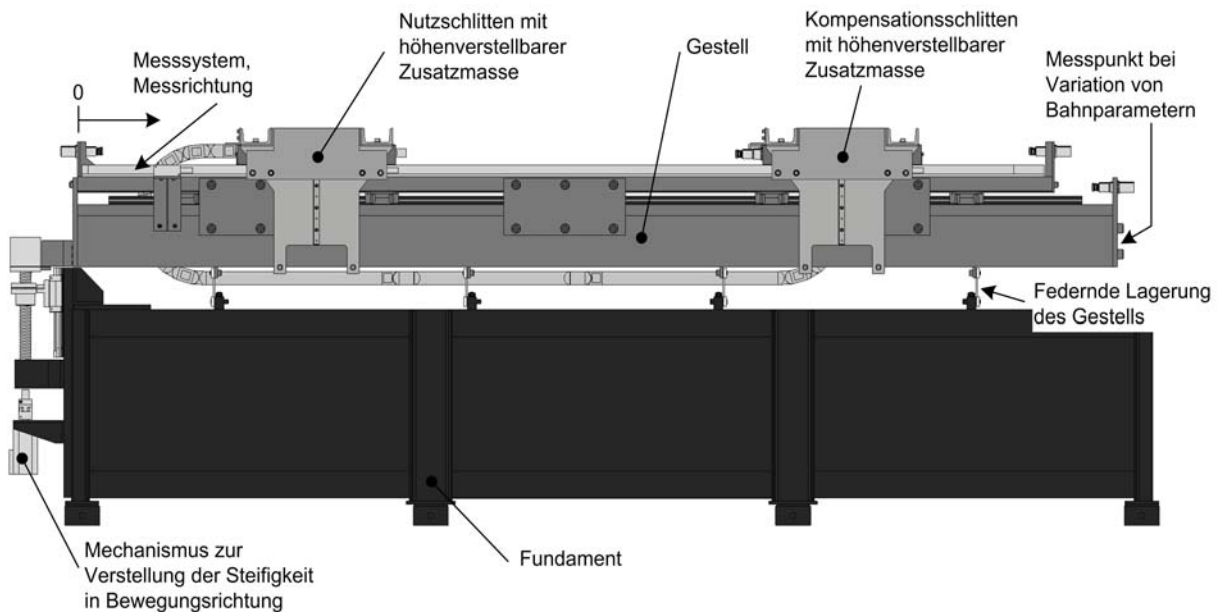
Versuchsstand zur Impulskompensation einer linearmotorgetriebenen Maschinenachse
